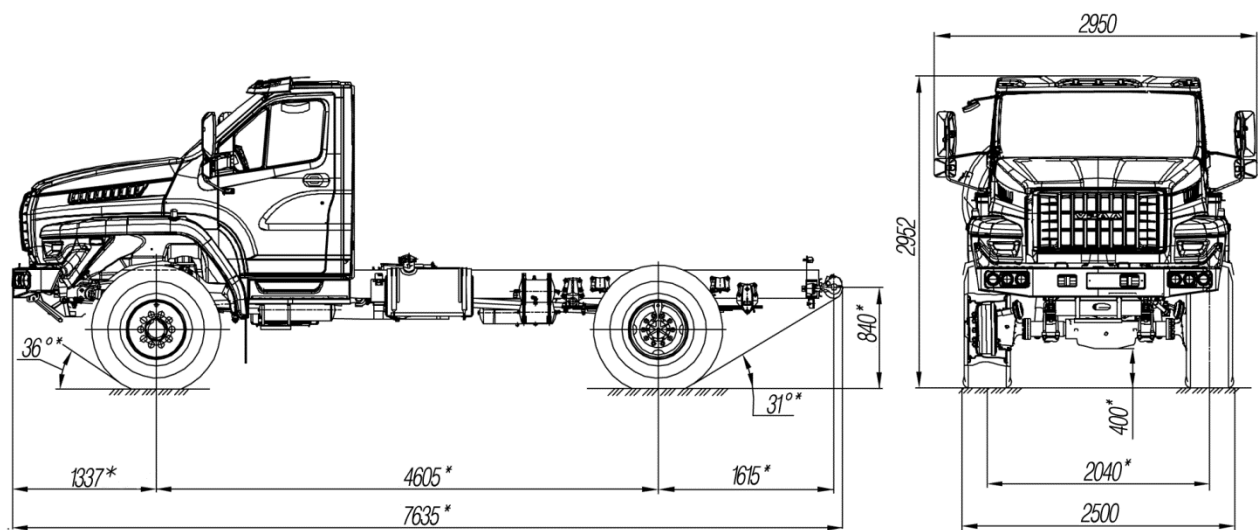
Габаритные размеры шасси Урал-43206-6151-71
